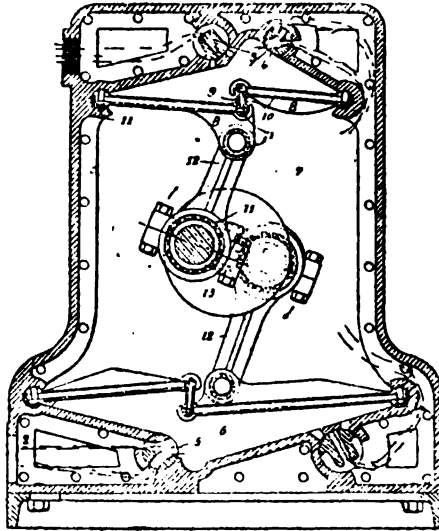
Coupe d'une machine compound de 25 chevaux.
